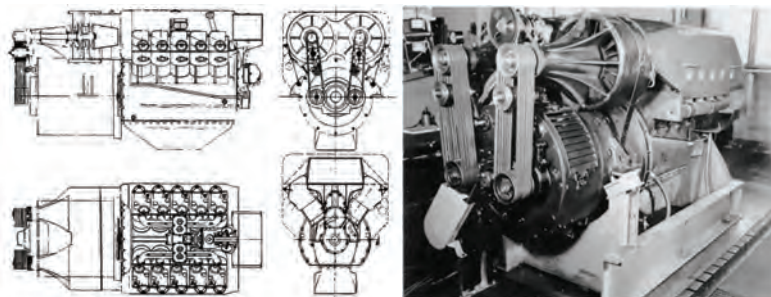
Двигатель танка «Tiger (P) Type 101»
